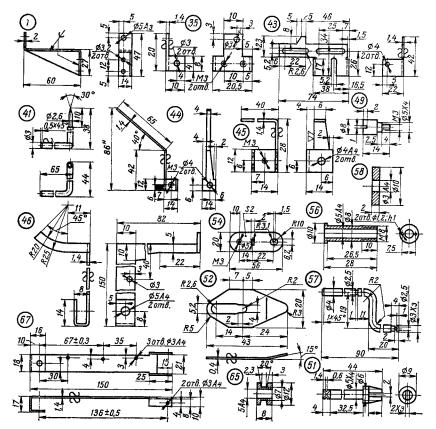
Детали переключателя формата, микролифта, механизма перемещения взукоснимателя и узла стыковки: 1— кронштейн, Ст. 3, после пайки цинковать; 35—скоба, Ст. 3; 41— стержень стыковочный, Ст. 3; 43—скоба, Ст. 3; 44—рычаг узла стыковки, Ст. 3, закрепить на дет. 57 винтом МЗ × 10; 45—рычаг, Ст. 3, закрепить так же на дет. 57; 46— рычаг микролифта, Ст. 3, хромировать; 49— поводок, Ст. 3; 51—ось ручки переключателя, Ст. 3; 52— пружина, Ст. 65Г; 54— планка переключателя, Ст. 3; 56— втулка, Ст. 3, хромировать; 57—рычаг, Ст. 3; 58—ролик, ЛС 59-1; 65—ролик, ЛС 59-1; 67—рычаг, Ст. 3. Стальные детали (кроме 1, 46 и 56) воронить.
